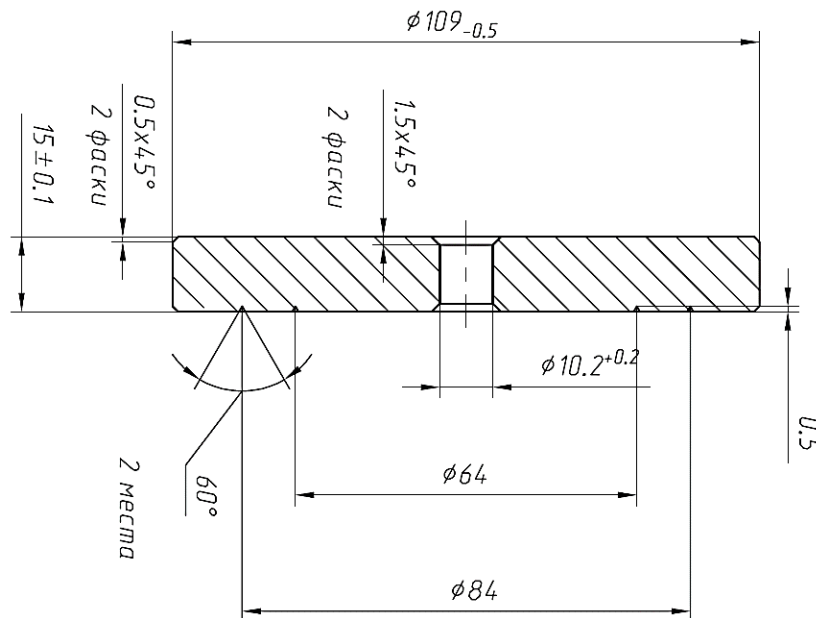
Опытный образец зубчатого колеса для отработки режима ЭЛС
